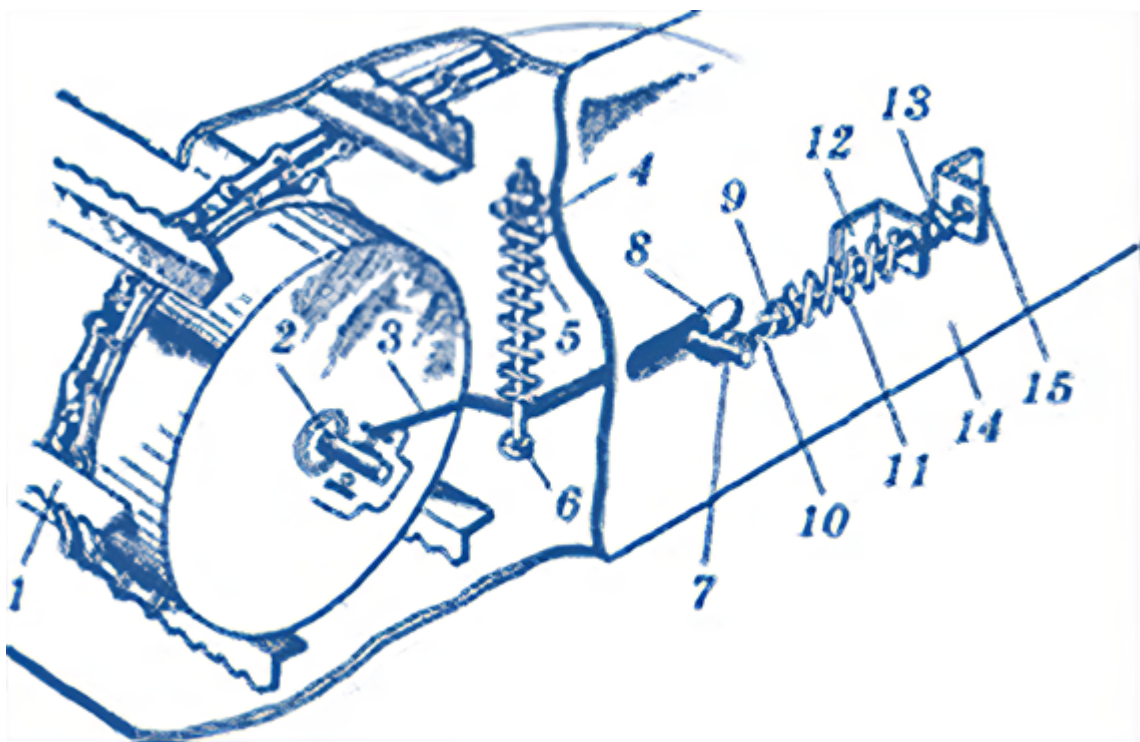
Схема підвіски веденого барабана плаваючого конвеєра:
